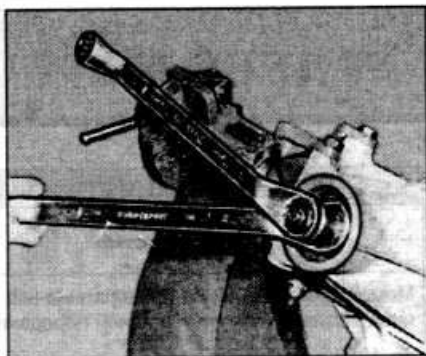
Отвертывание стопорной гайки ведущей шестерни главной передачи оправкой 15.073 и накидными ключами «на 32» и «на 36»
